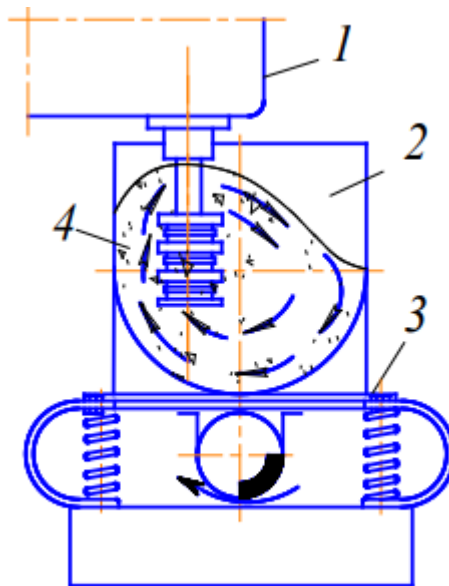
Схема процесу шпиндельної віброабразивної обробки: 1 – шпиндель верстата; 2 – робоча камера (бункер); 3 – вібраційна установка; 4 – оброблювана деталь
